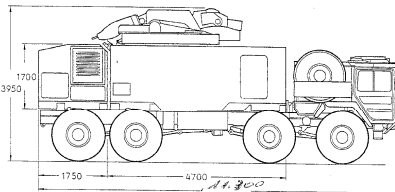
Abmessungen FlaRaKRad, Seitenansicht
